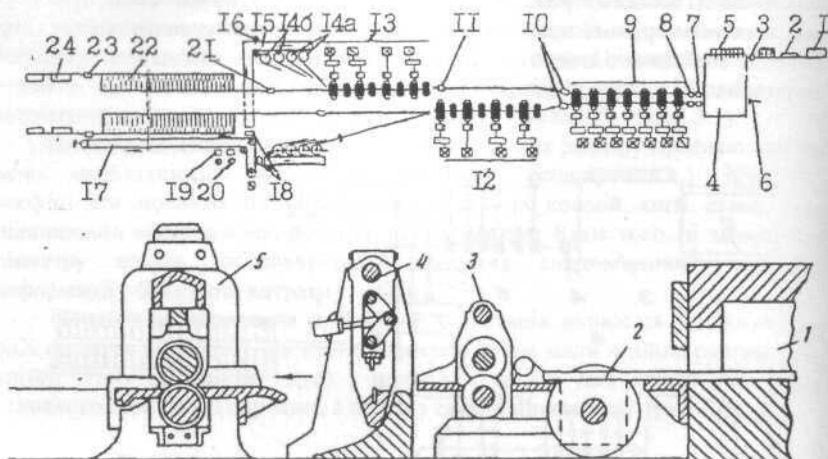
Схема розташування устаткування неперервного двохниткового стана 250: 1 - приймальні грати; 2 - карман для брака; 3 - штовхач заготовок у піч; 4 - нагрівальна піч; 5 - штовхач т; 6 - виштовхувач; 7 - розподільний пристрій; 8 - ножиці; 9 - чорнова група клітей; 10 - летучі ножиці кривошипного типу; 11 -обривні ножиці; 12,13 - неперервні чистові групи клітей; 14 - стрічкові і сортові моталки; 15 - пластинчатий конвейер; 16 - бунтовязальні машини; 17 - конвейер крюковий; 18 - бунтонавешувач; 19 - бунтосъемний пристрій; 20 - пакетуюча машина; 21 - одновісні летучі ножиці; 22 - холодильник; 23 - эксцентрикові ножиці холодного різання; 24 - карман.
